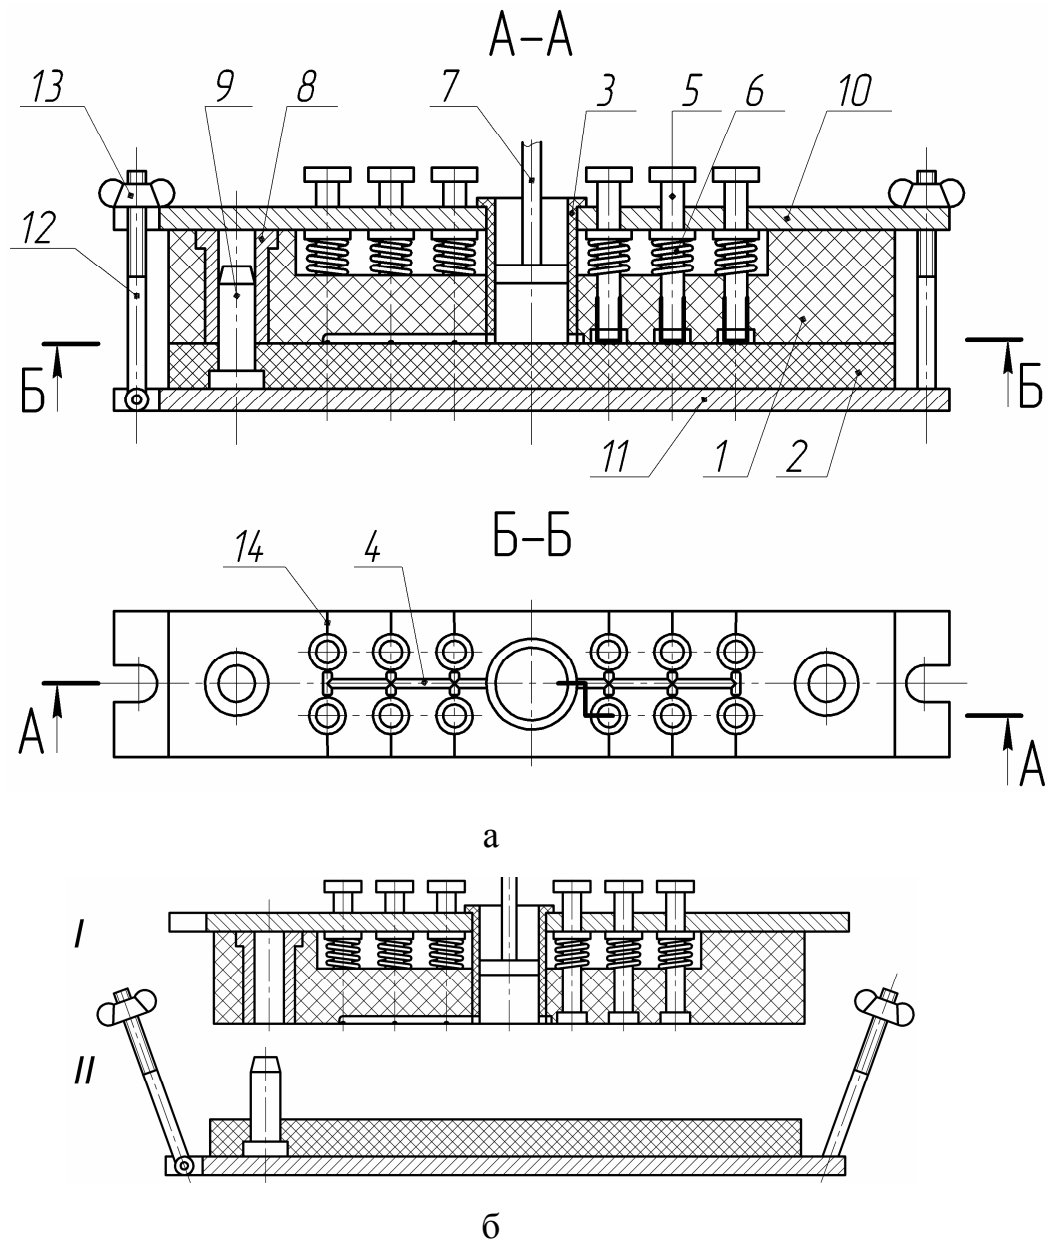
Конструкція дванадцятигніздної форми для виготовлення виробів з
